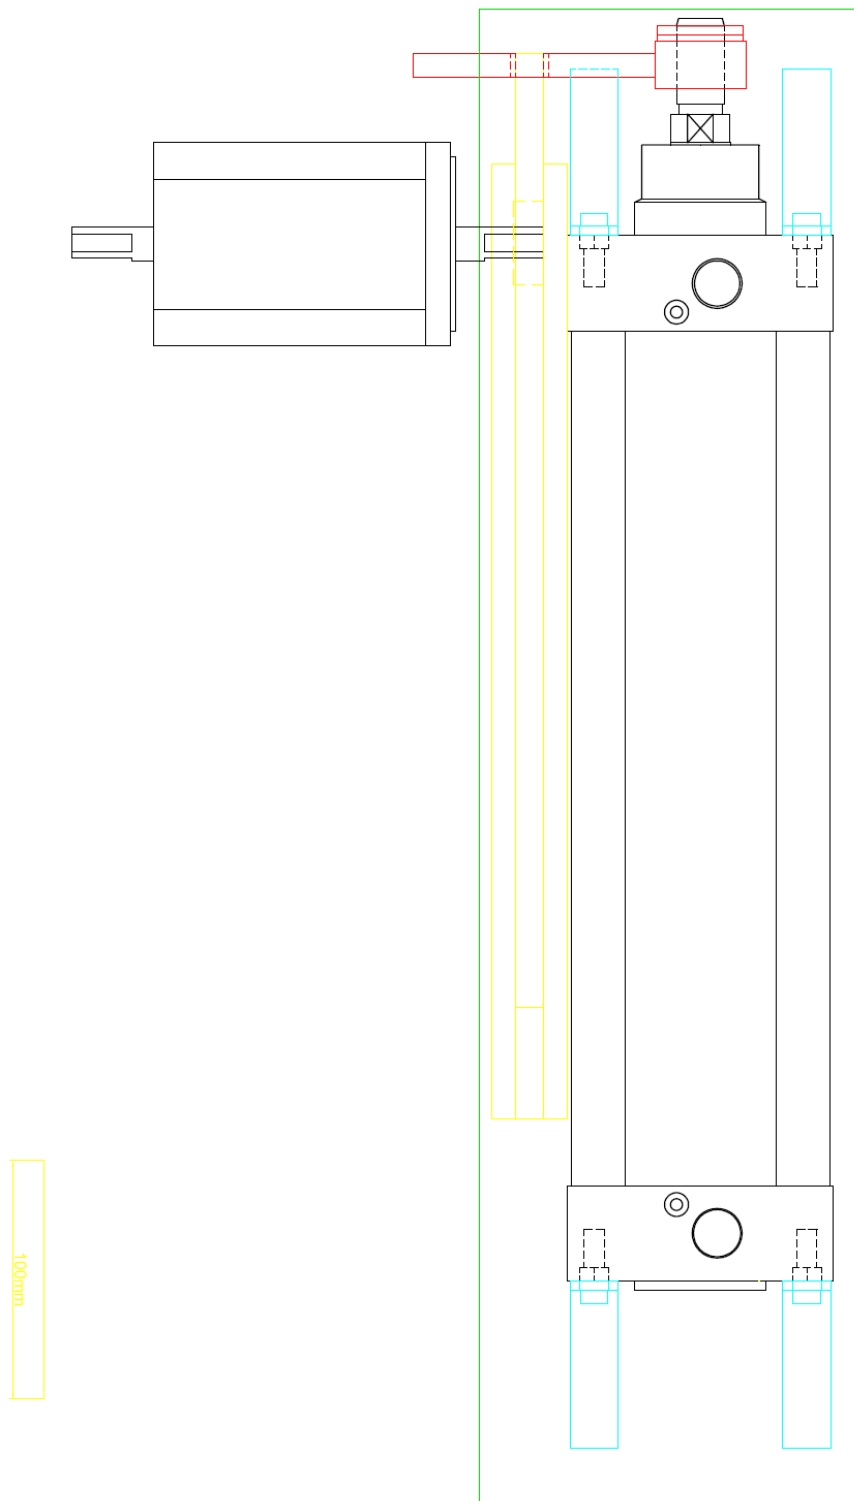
SIMVENT, parte mecánica vista superior - fuente SIMVENT
